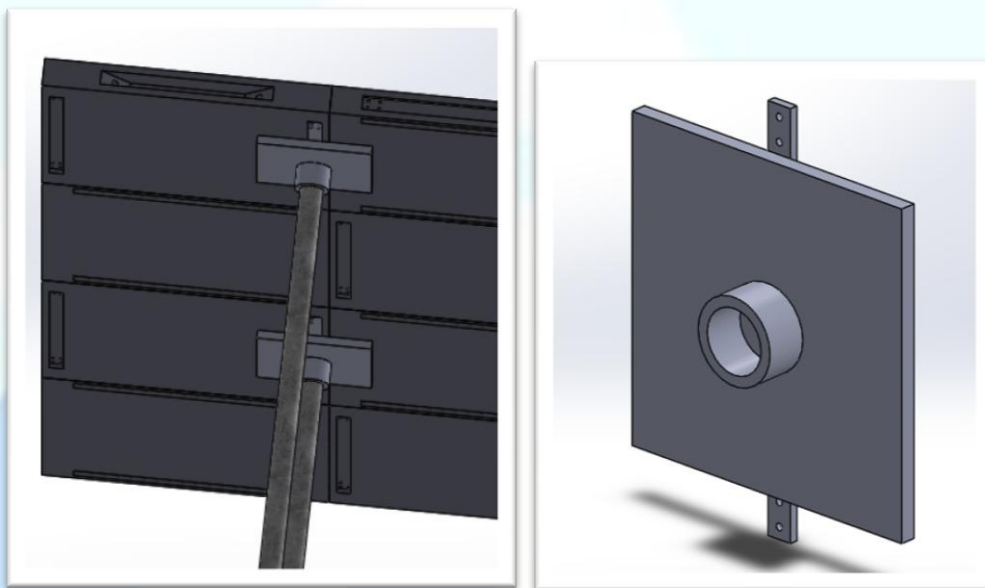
ensamblaje con elementos auxiliares (izquierda), elemento auxiliar (derecha)
